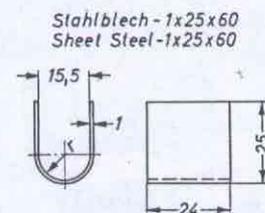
Abstandblech für Schaltgabel des 2. und 3. Ganges
